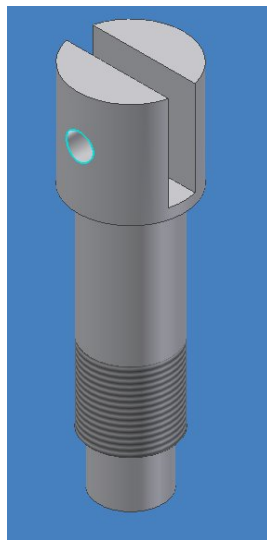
Pièce d'amarrage des éprouvettes forgées.
